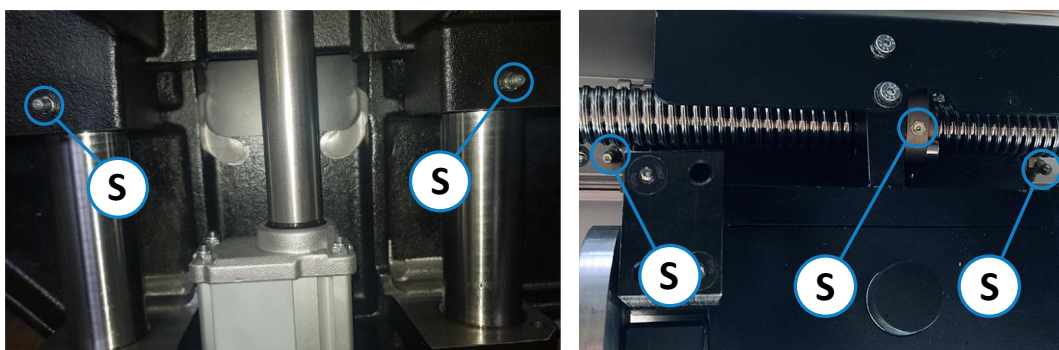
points de lubrification sur le réglage en hauteur et sur la broche de guide parallèle
